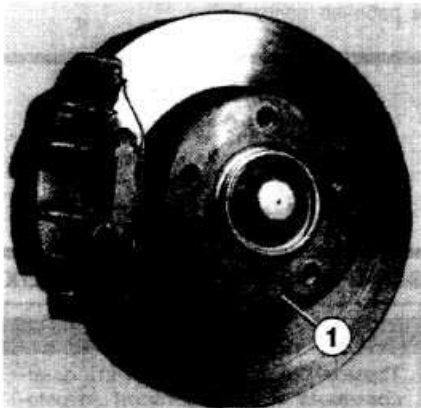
Болт 1 крепления диска переднего тормоза
